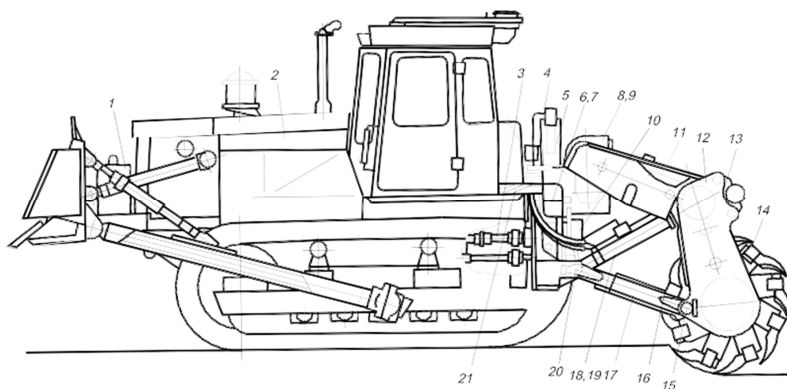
Машина для фрезерования почвы: 1 – противовес; 2 – трактор; 3 – привод рабочего органа; 4 – гидрораспределитель; 5 – гидропривод ходоуменьшителя; 6 – управление; 7 – управление приводом рабочего органа; 8 – редуктор отбора мощности; 9 – редуктор ходоуменьшителя; 10 – предохранительная муфта; 11 – тяга; 12 – бортовой редуктор; 13 – балка; 14 – рабочий орган; 15, 16 – цепная передача; 17 – рама; 18 – гидропривод; 19 – гидропривод подъема и опускания; 20 – оси; 21 – управление распределителем ходоуменьшителя
